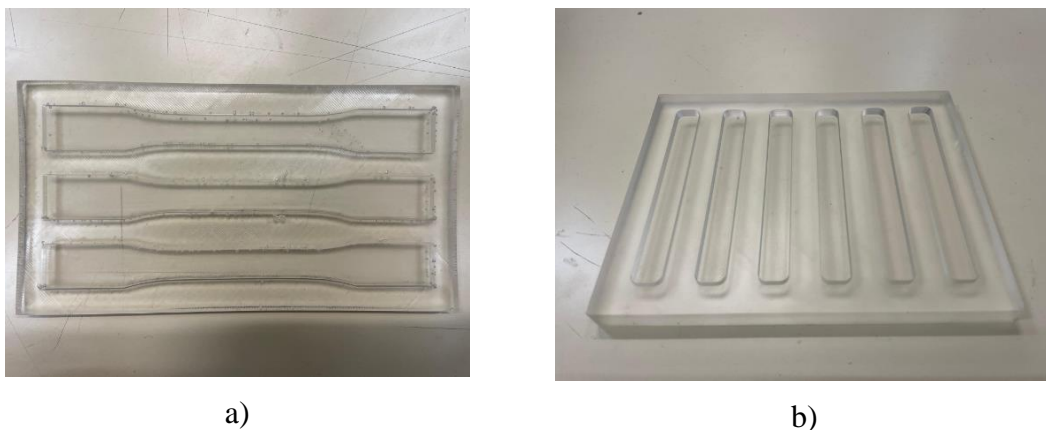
Moldes para fabricação de corpos de prova de a) tração e b) flexão
